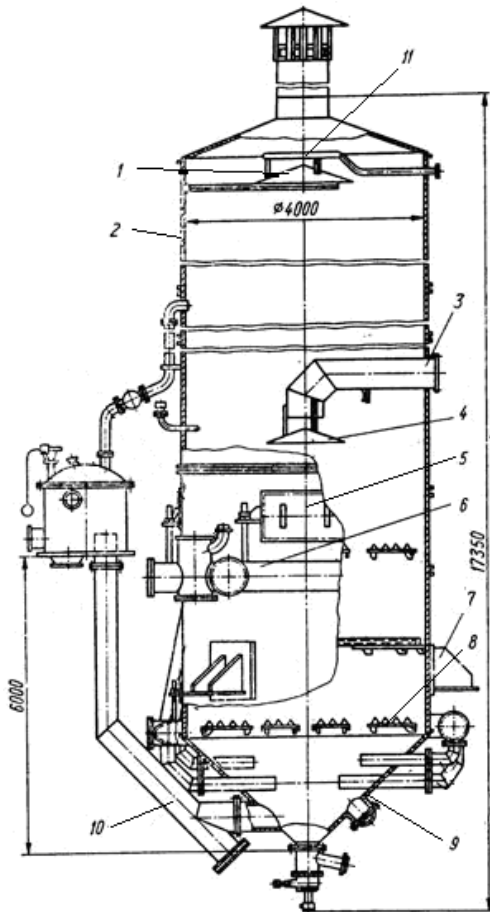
Сатуратор 1С-6: 1 – відбивний зонт; 2 – корпус; 3 – труба для підведення соку; 4 – розподільвальний зонт; 5 – люк; 6 – труба для підведення газу; 7 – опора; 8 – решітка; 9 – конічне днище; 10 – відвідна труба; 11 – барботер парового піногасника.
